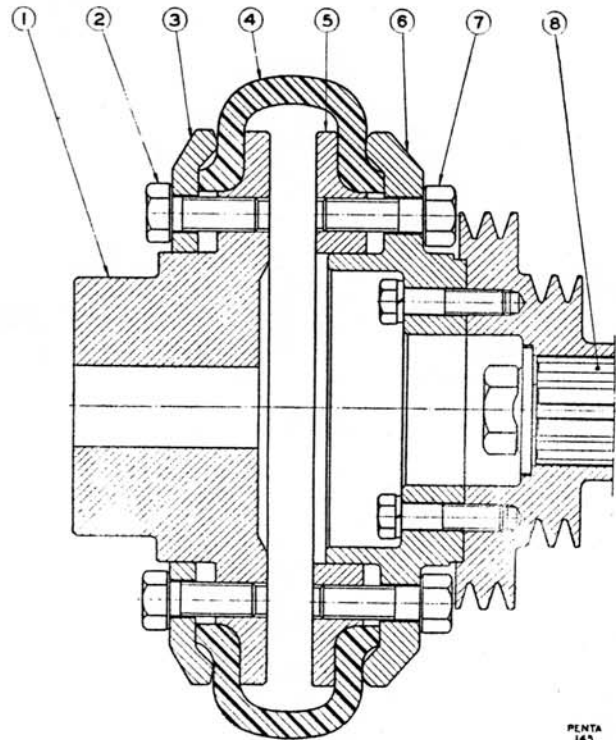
Elastische Kupplung für die Frontseite des Motors im Schnitt.
